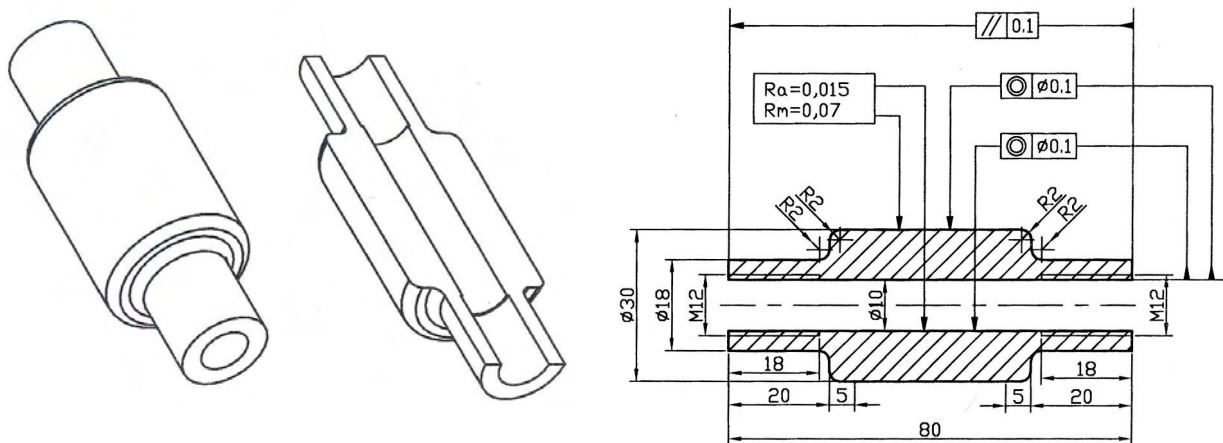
Schéma des éprouvettes tubulaires de fatigue thermique (dimensions en mm).
